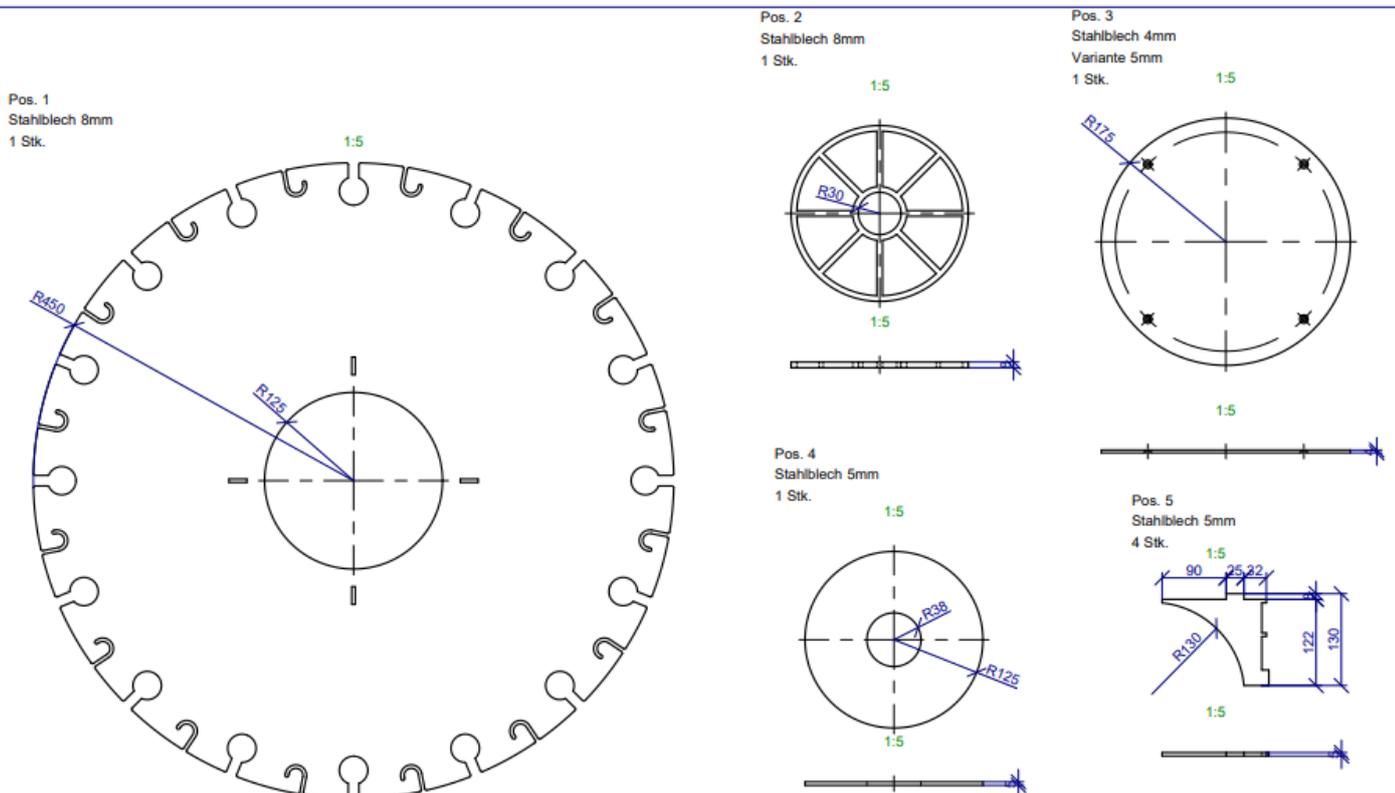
Plan Fonduefass, Elena Schumann, 15. Dezember 2021
